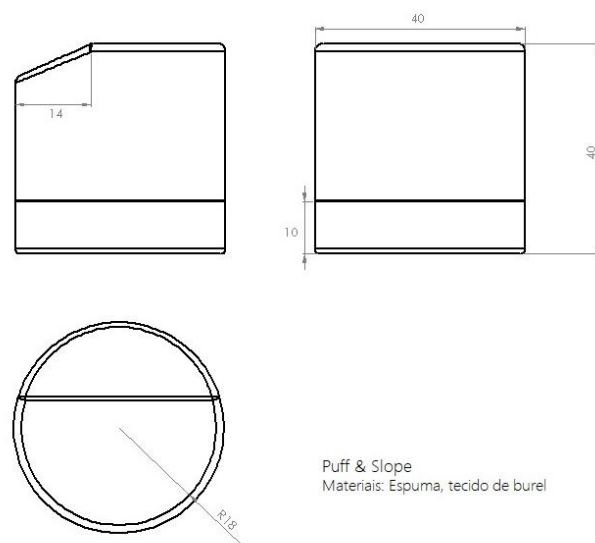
Desenho técnico CAD 3D do conceito (Fonte: Autor)
